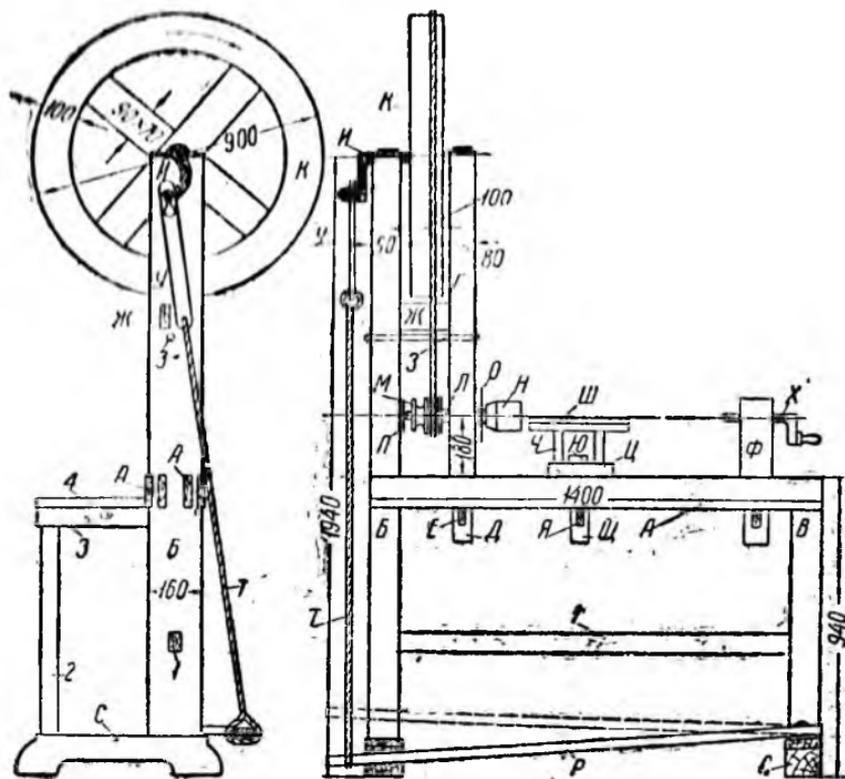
Самодельный универсальный токарный станок (справа—вид спереди, слева—вид сбоку)
